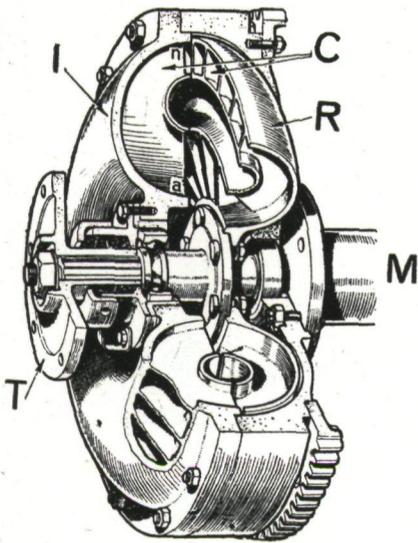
M, extremo del cigüeñal del motor. I, volante con los álabes del impulsor. R, rotor. C, celdas del turbo-embrague. T, lado de la transmisión.
